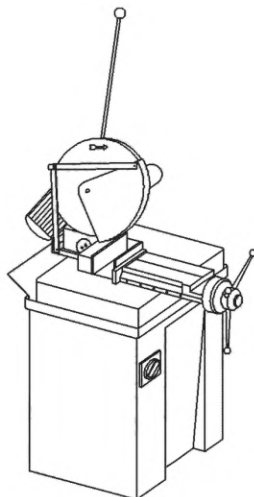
Круглопильный станок с ручной подачей — тип с поворотной головкой
